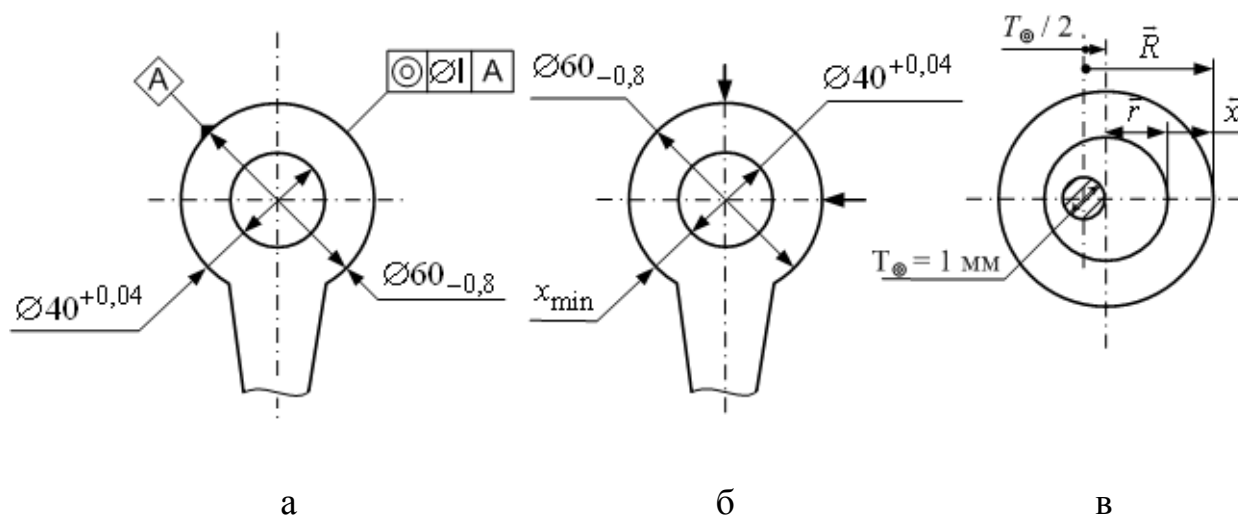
Размерная цепь допусков размеров и расположения:
